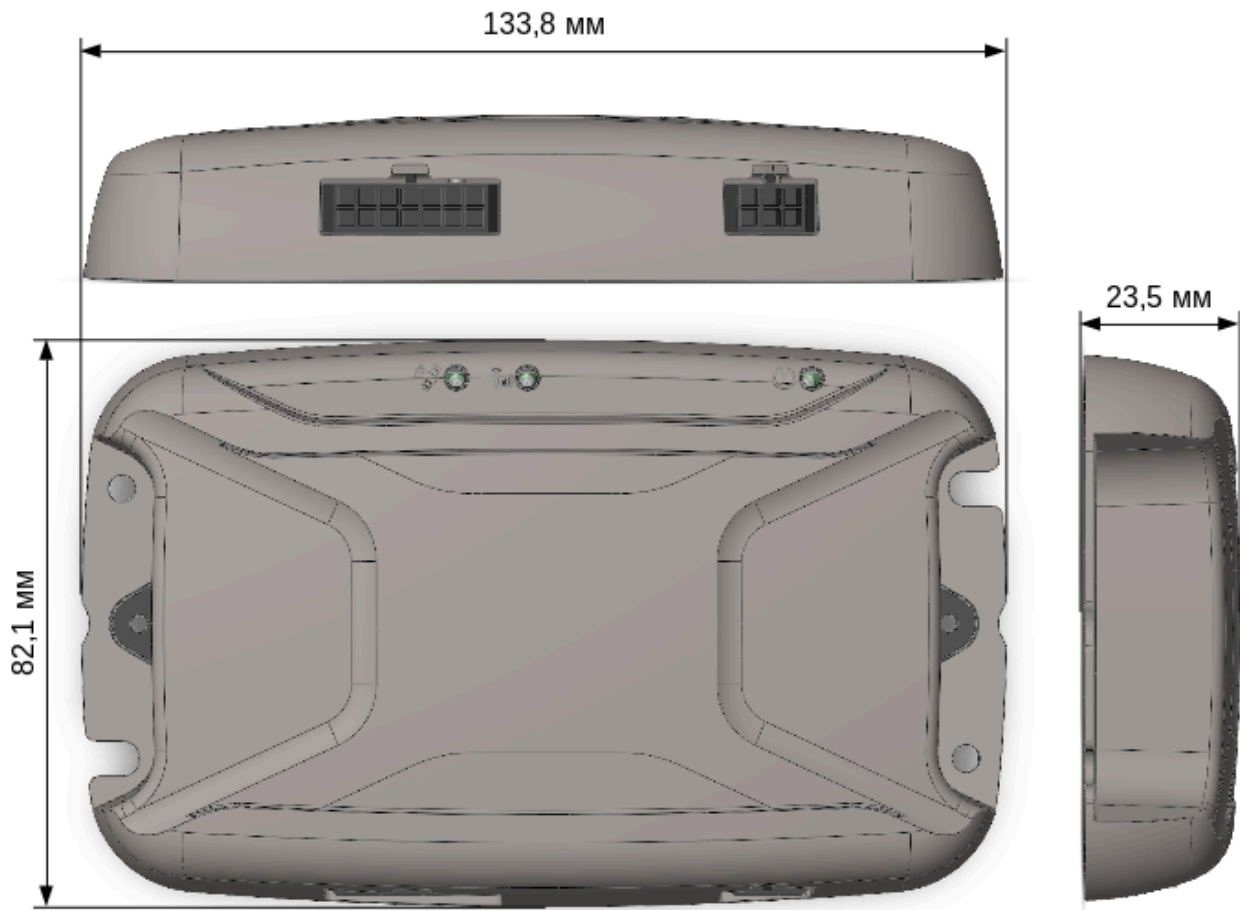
Внешний вид корпуса основного блока и габаритные размеры.
